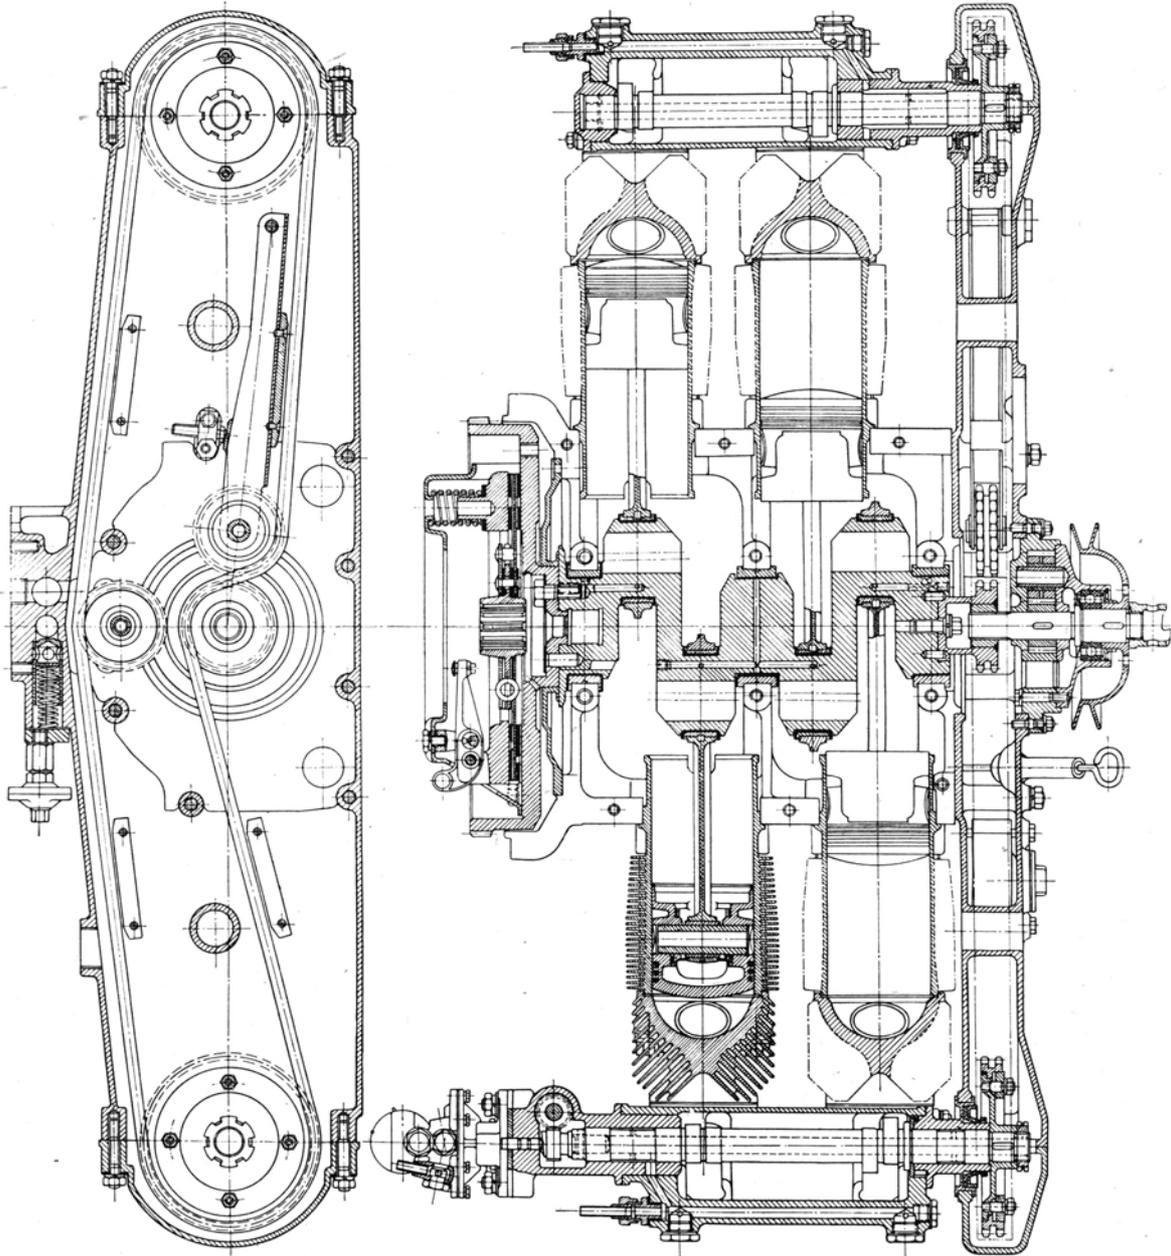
Langsschnitt und Schnitt durch den Nockenwellenantrieb zum Motor Abb. 149
